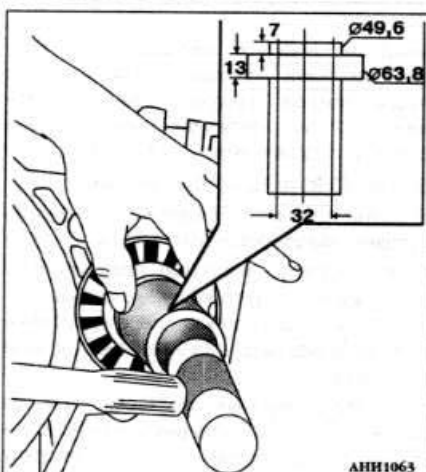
Запрессовка сальника выходного вала дифференциала
